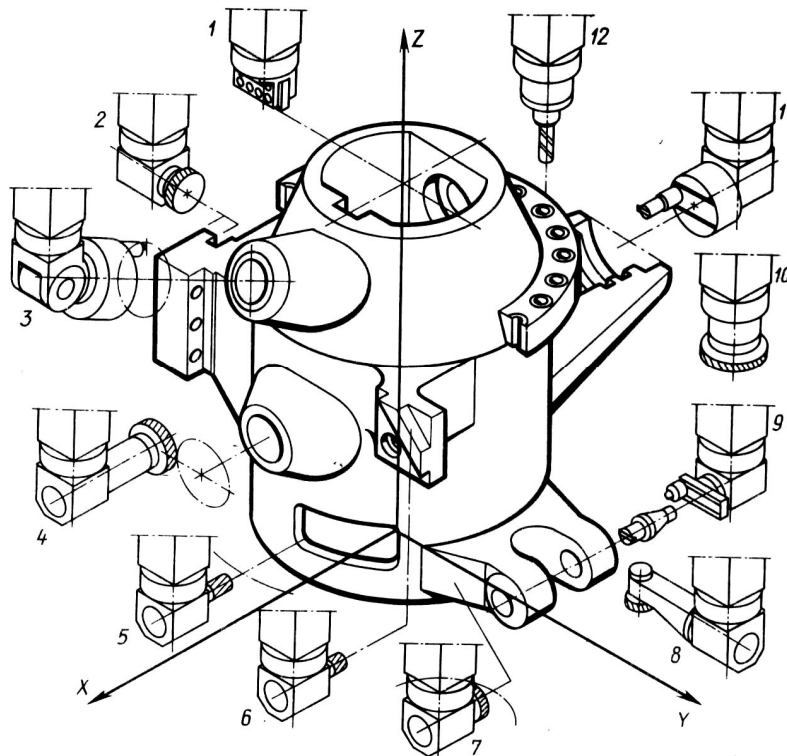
Схема технологических переходов, выполняемых на многоцелевом станке карусельного типа при обработке крупногабаритной заготовки корпусной детали: 1 – карусельное точение по цилиндрическим и плоским горизонтальным поверхностям; 2, 3 – фрезерование привалочных поверхностей; 4 – фрезерование торцов; 5 – контурное фрезерование бокового окна; 6 – фрезерование уступов; 7, 8 – фрезерование поверхностей приливов; 9 – растачивание отверстий, обработка торцов; 10 – фрезерование плоскости разъема; 11 – прорезка канавок резцом; 12 – сверление и зенкерование малых отверстий, нарезание резьбы
